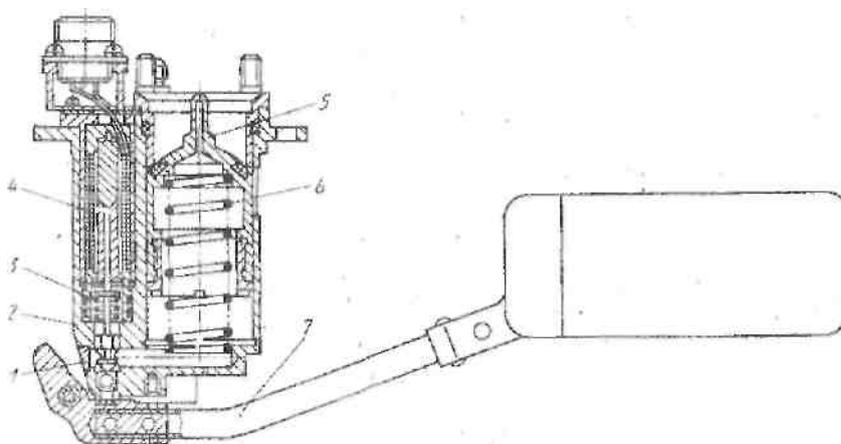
Узел заправки: 1 - шток; 2 - корпус; 3, 6 - пружины; 4 - электромагнитный клапан; 5 - плунжер; 7 - поплавковый клапан
